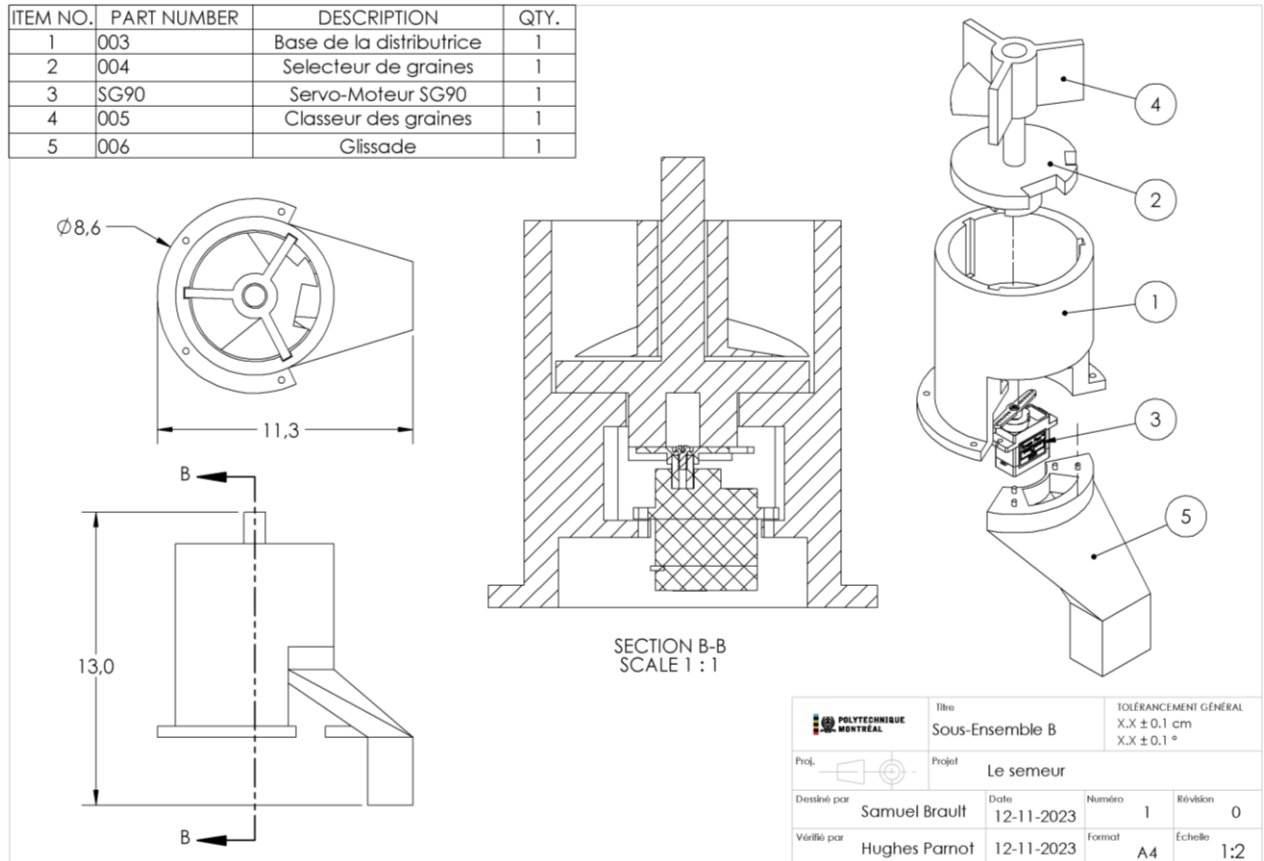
Dessin d'assemblage du Sous-Ensemble B
